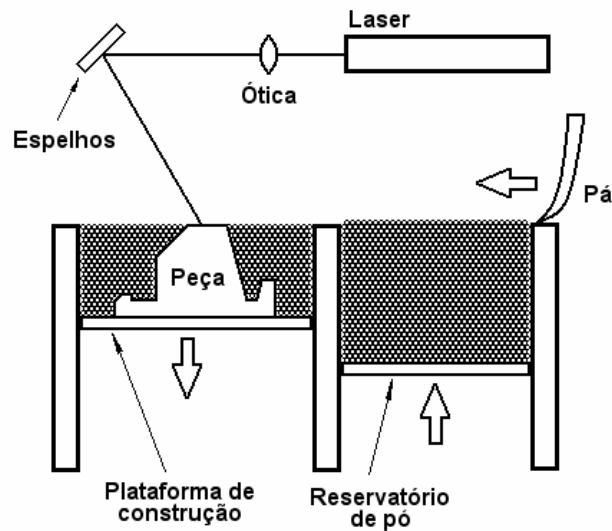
Desenho esquemático de um sistema de sinterização a laser [29].
